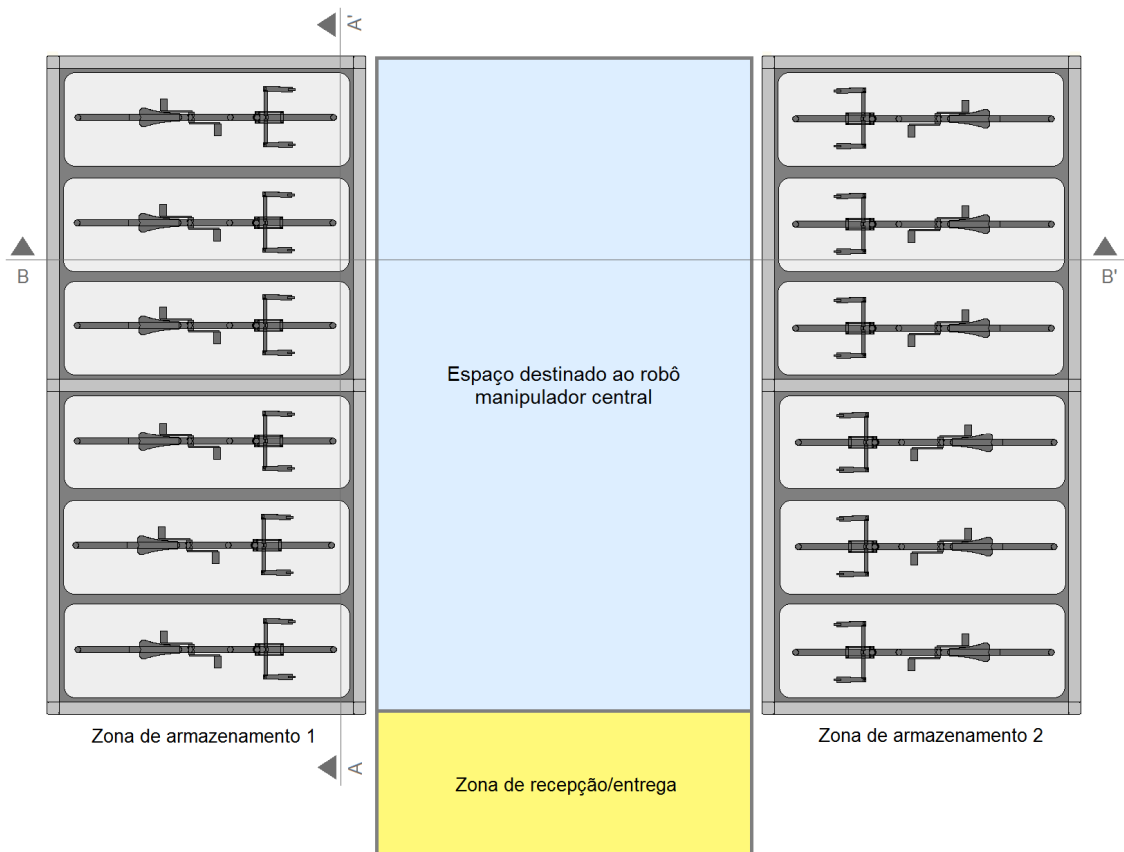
Configuração da estrutura adoptada - Vista em planta.
